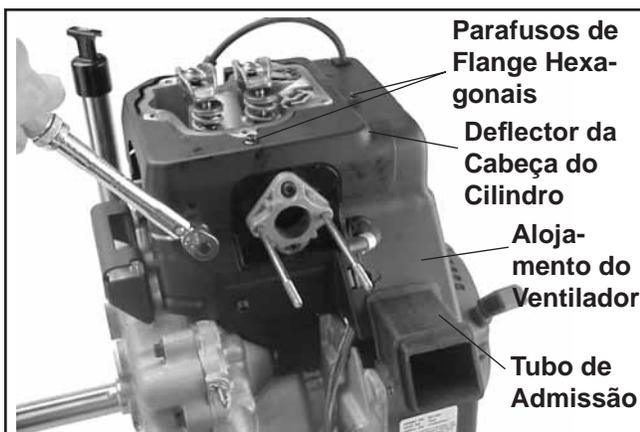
Instalar o Deflector da Cabeça do Cilindro e o Tubo de Admissão.
